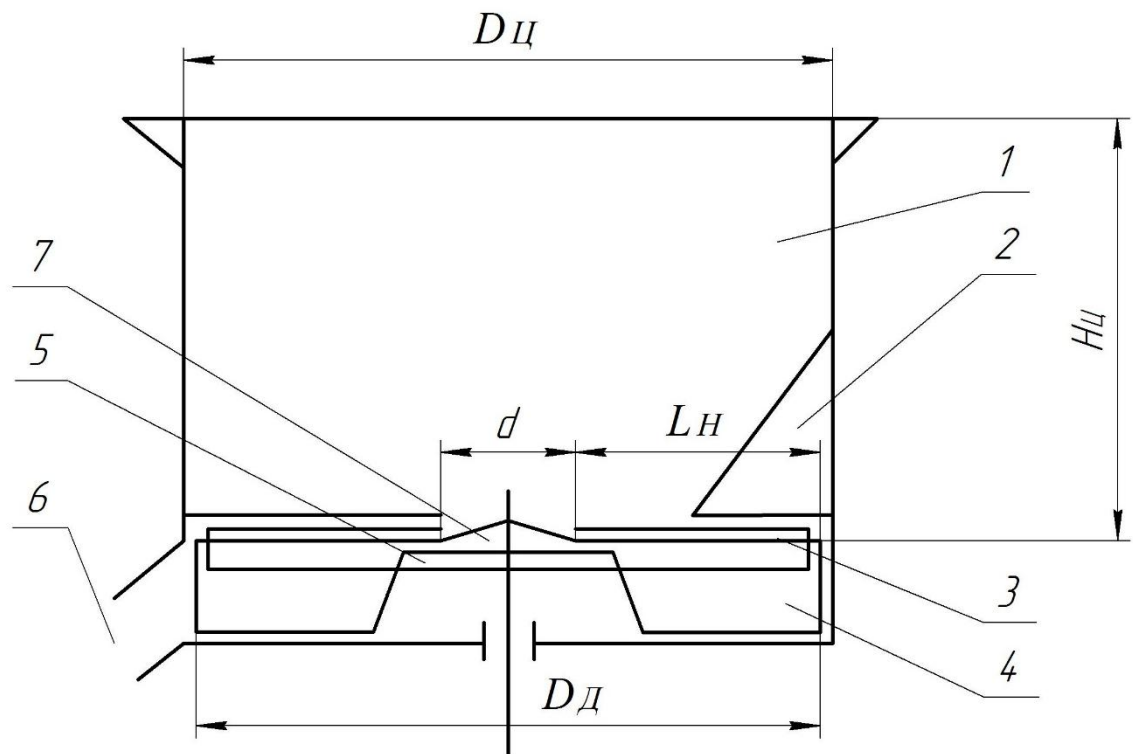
Конструктивна схема механізму порізки коренів:
